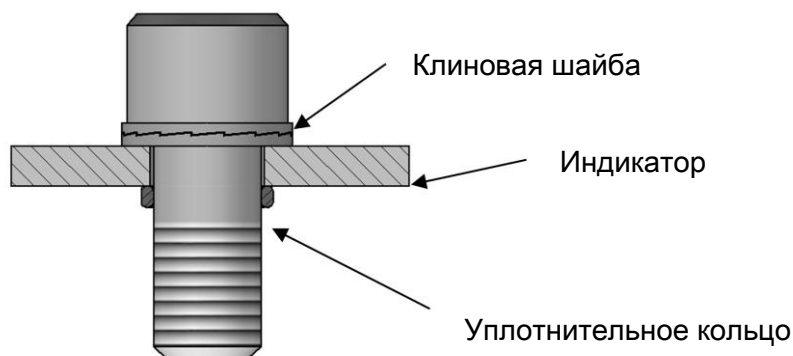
Расположение уплотнительного кольца и шайбы приводного винта
